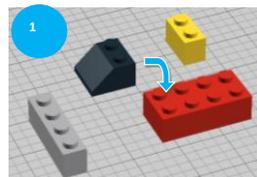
PLANO DE MONTAJE – CENTRO DE TRABAJO 3.
